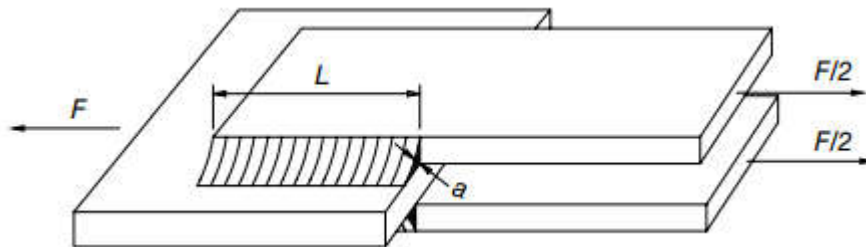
Plaques assemblées par cordons de soudure longitudinaux
